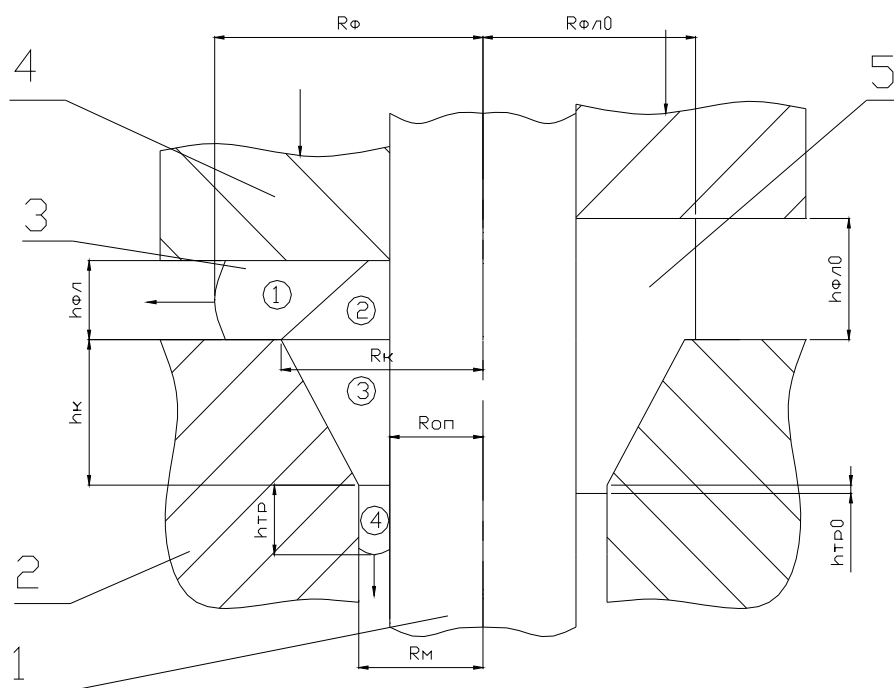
Схема комбинированного процесса высадки с прямым выдавливанием: 1 – оправка; 2 – матрица; 3 – получаемая деталь; 4 – пуансон; 5 – исходная заготовка.
